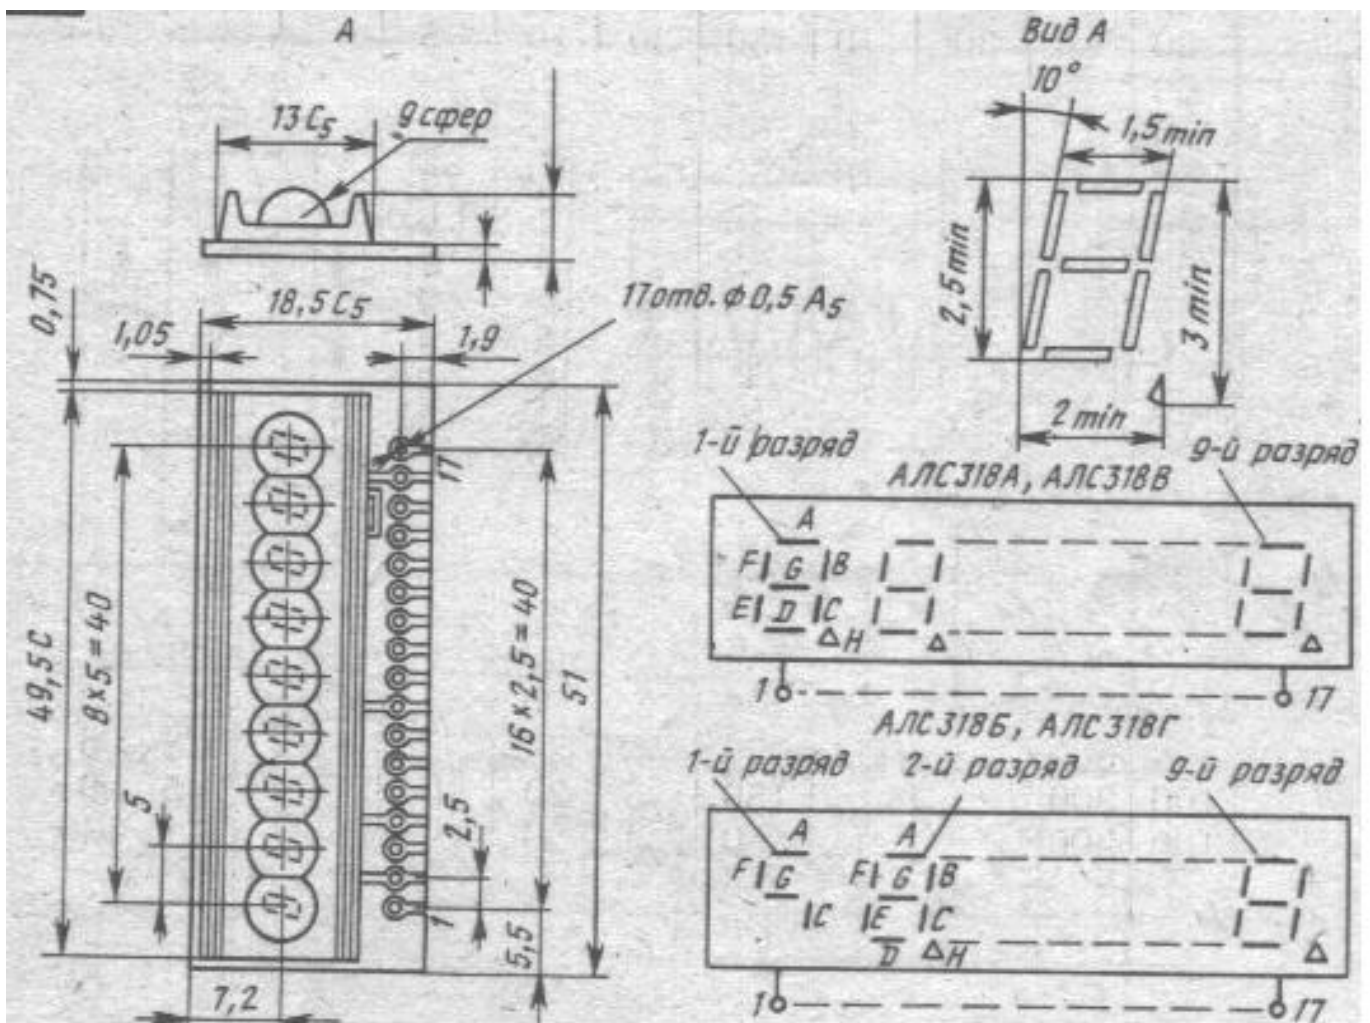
Внешний вид и типовые размеры индикатора АЛС318
